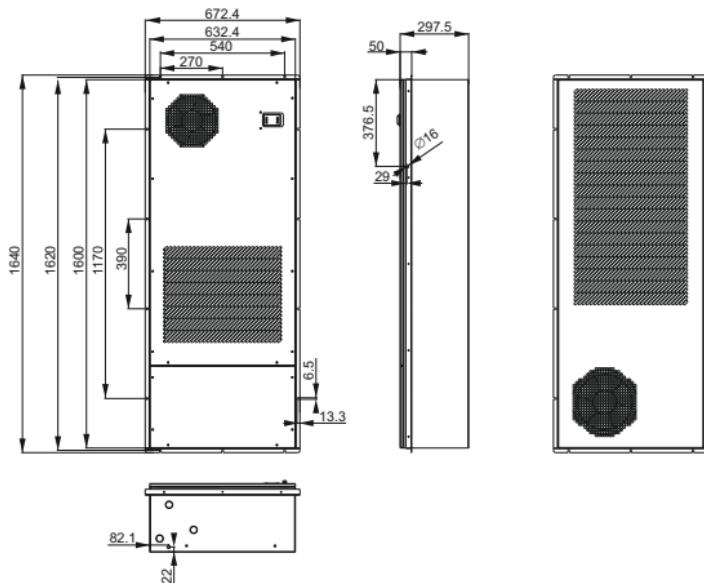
Внешний вид и габаритные размеры модели СМ-5000-380 / Figure 6 – Appearance and overall dimensions of CM-5000-380 version
